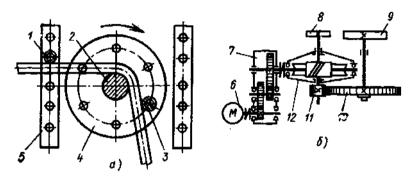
Станок для гнутья арматуры: а – схема работы станка для гнутья легкой арматуры; б – кинематическая схема станка для гнутья тяжелой арматуры
